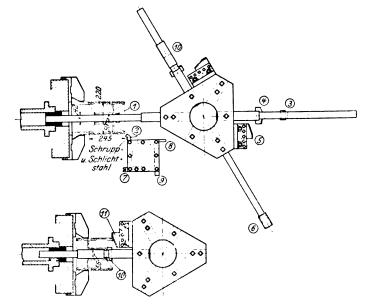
Bearbeitung von Lokomotiv-Schieberköpfen.
